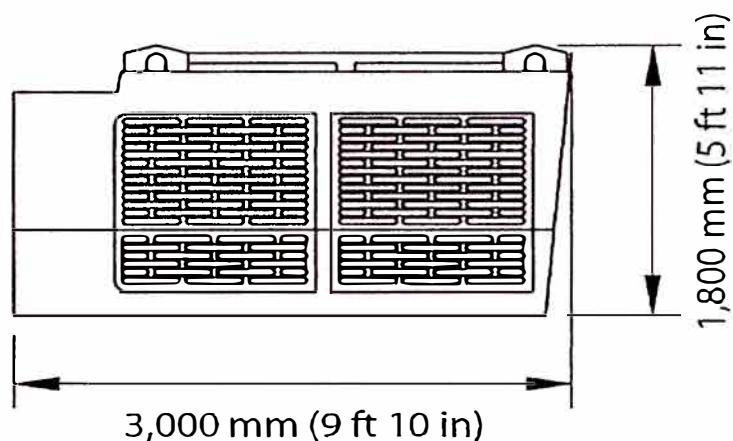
Dimensiones del Módulo de Enfriamiento
